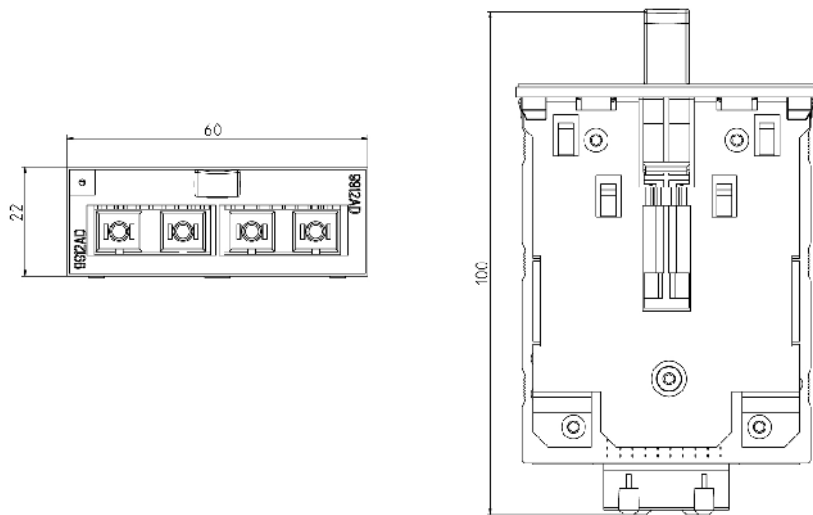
MM900 Dessin coté 4 : Ports optiques SC
